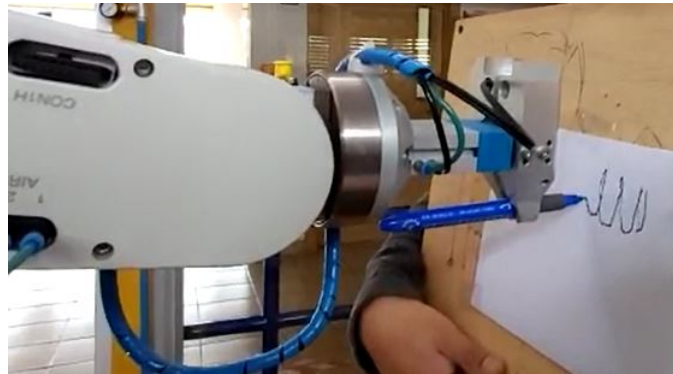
Robot Mitsubishi RV-2AJ dibujando trayectoria de soldadura (Fuente propia)
